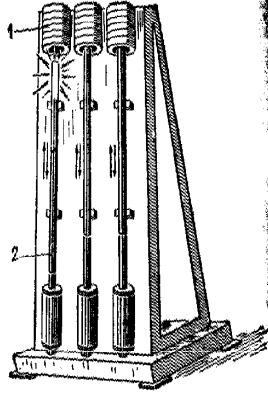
Схема нагревателя фирмы «АЕГ» для нагрева концов штанг:
